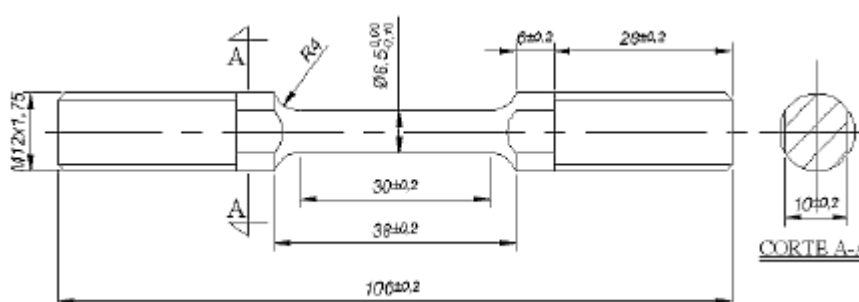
Geometria e dimensões dos corpos de prova utilizados nos ensaios de tração em temperatura ambiente e em alta temperatura no metal base e junta soldada, nos corpos de prova da junta soldada, a solda é localizada no centro do comprimento útil do corpo de prova.
